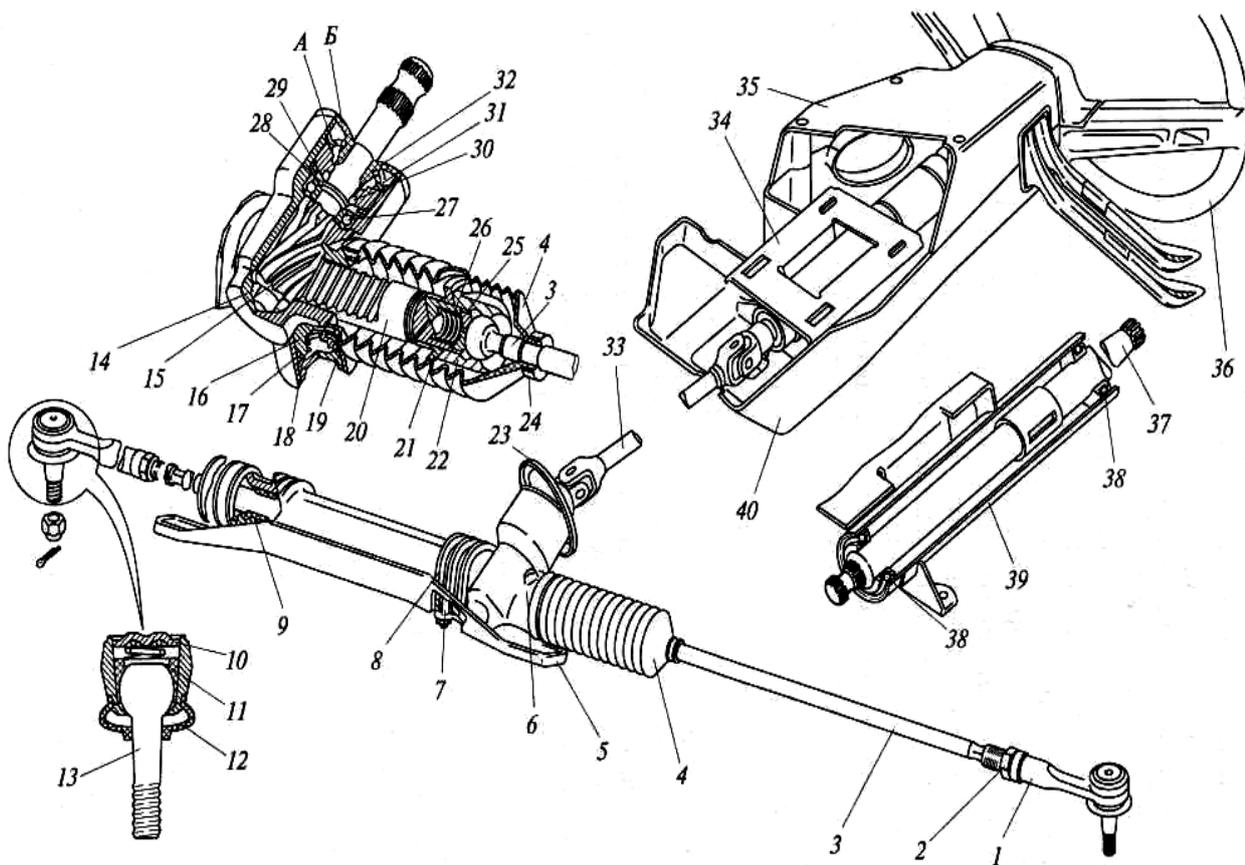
Рулевое управление типа шестерня—рейка: 1; и 7 - наружный и внутренний наконечники рулевой тяги; 2, 21 — контргайки; 4 — защитный чехол; 5, 8 — опоры рулевого механизма; 6 — картер рулевого механизма; 7 — хомут крепления рулевого механизма; 9 — втулка рейки; 10 — опорная шайба; 11 — вкладыш шарового пальца; 12 — защитный колпачок; 13- ; 14 — роликовый подшипник; 15 — приводная шестерня; 16 — упор рейки; 17 — уплотнительное кольцо упора; 18 — рейка упора; 19 — стопорное кольцо гайки; 20- ; 22 — шаровая опора; 23 — уплотнитель вала; 24 — хомут чехла; 25 — упор тяги; 26 — пружина упора; 27 — шариковый подшипник; 28 — стопорное кольцо; 29 — защитная шайба; 30 — уплотнительное кольцо; 31 — гайка крепления подшипника; 32 — сальник; 33 — промежуточный карданный вал; 34 — кронштейн крепления вала рулевой колонки; 35 и 40 — верхний и нижний облицовочные кожухи; 36- ; 37 — вал рулевой колонки; 38- подшипники вала рулевой колонки; 39 — труба рулевой колонки; А, Б — метки на картере рулевого механизма и пыльнике.
